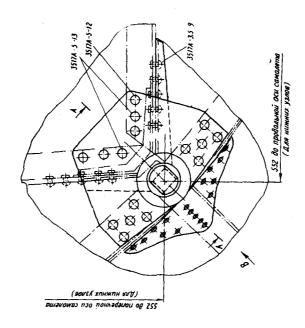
Установка узла крепления моторамы на шп. № 1 на самолетах до сер. № 1Г112-01: 1— уголок Ш0106-4 (для верхних узлов) или Ш0107-4 (для нижних); 2— прокладка Д16АТ-л.0,3-2,0 мм (при необходимости); 3— ухо Ш0106-13-1 (нижнее правое), Ш0106-13-2 (нижнее левое), Ш0106-13-3 (верхнее правое), Ш0106-13-4 (верхнее левое); 4— накладка Ш0106-1; 5— кница Ш0106-2-1/2 (верхняя) или Ш0107-2-1/2 (нижняя)
